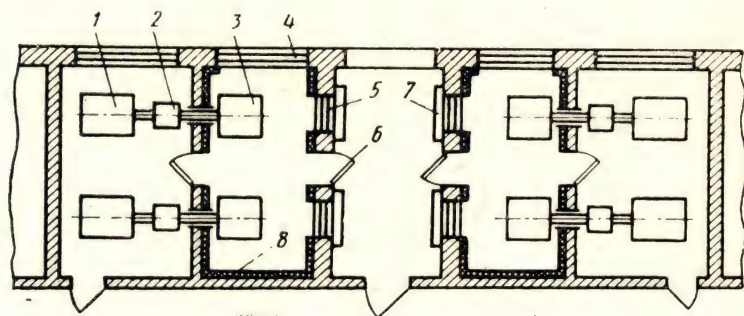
План расположения испытательного стенда схемы привод — мультипликатор — испытуемый агрегат:
